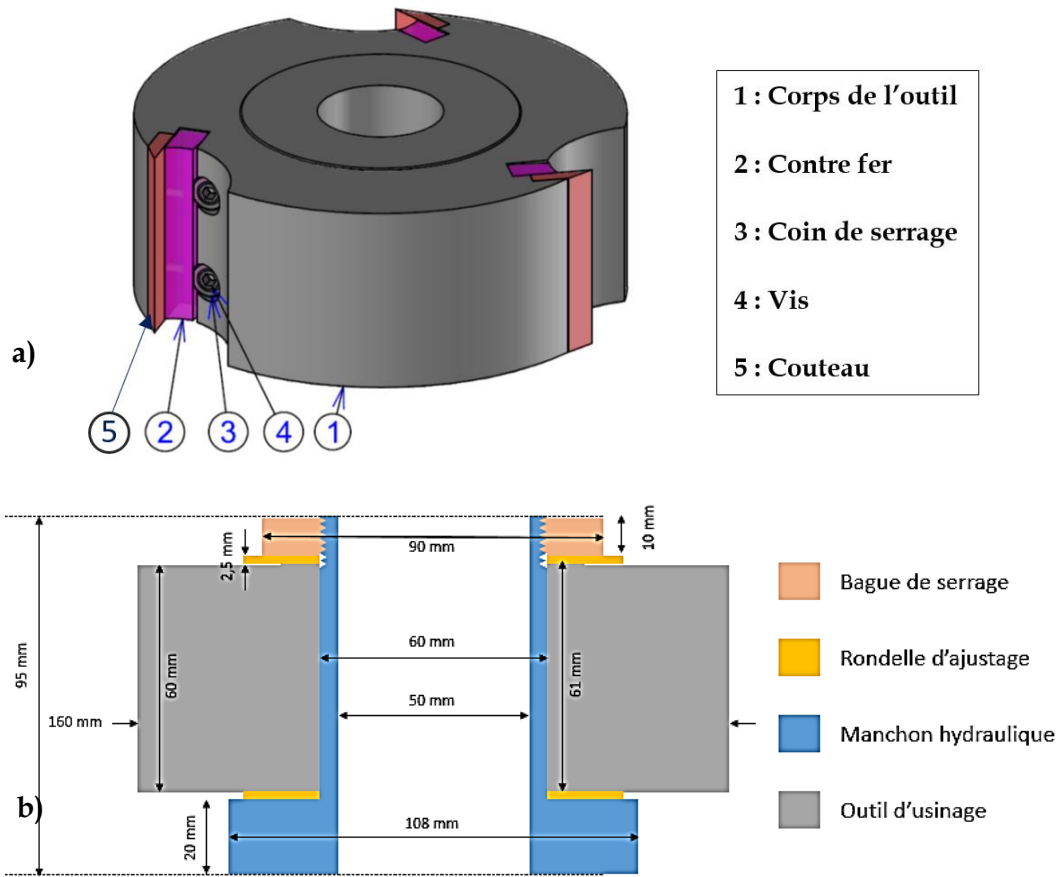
Outil utilisé pour l'usinage sur le banc TEEMO a) vue 3D de l'outil et b) montage de l'outil.
